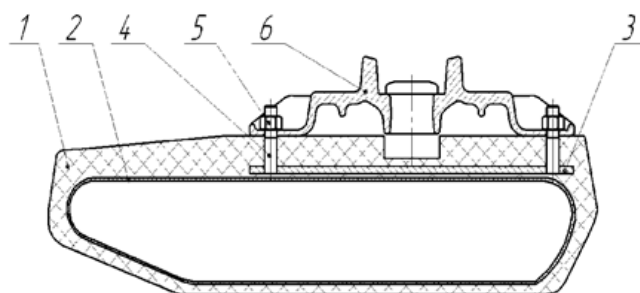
Гусеница трактора ВТ-150, продольный разрез:
